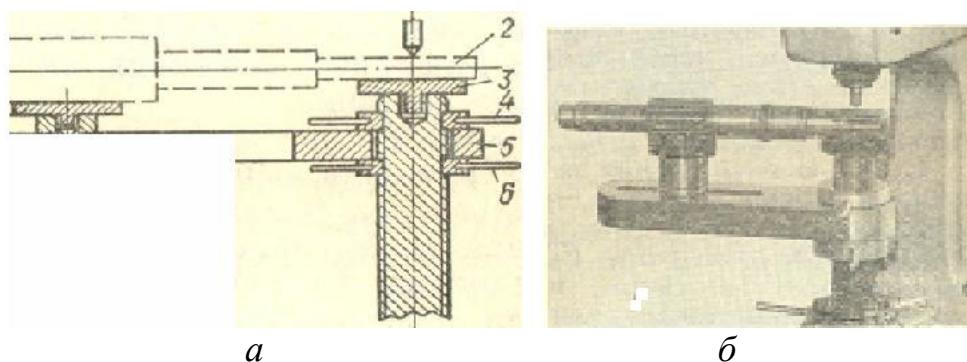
Приспособа для вимірювання твердості довгомірних деталей на твердомірі Роквела: а – схема приспособи: 1 і 3 – підтримуючий і опорний столики; 2 – деталь; 4 і 6 – прижимна і опорна гайка; 5 – кронштейн; б – загальний вигляд установки приспособи на столику твердоміра.
